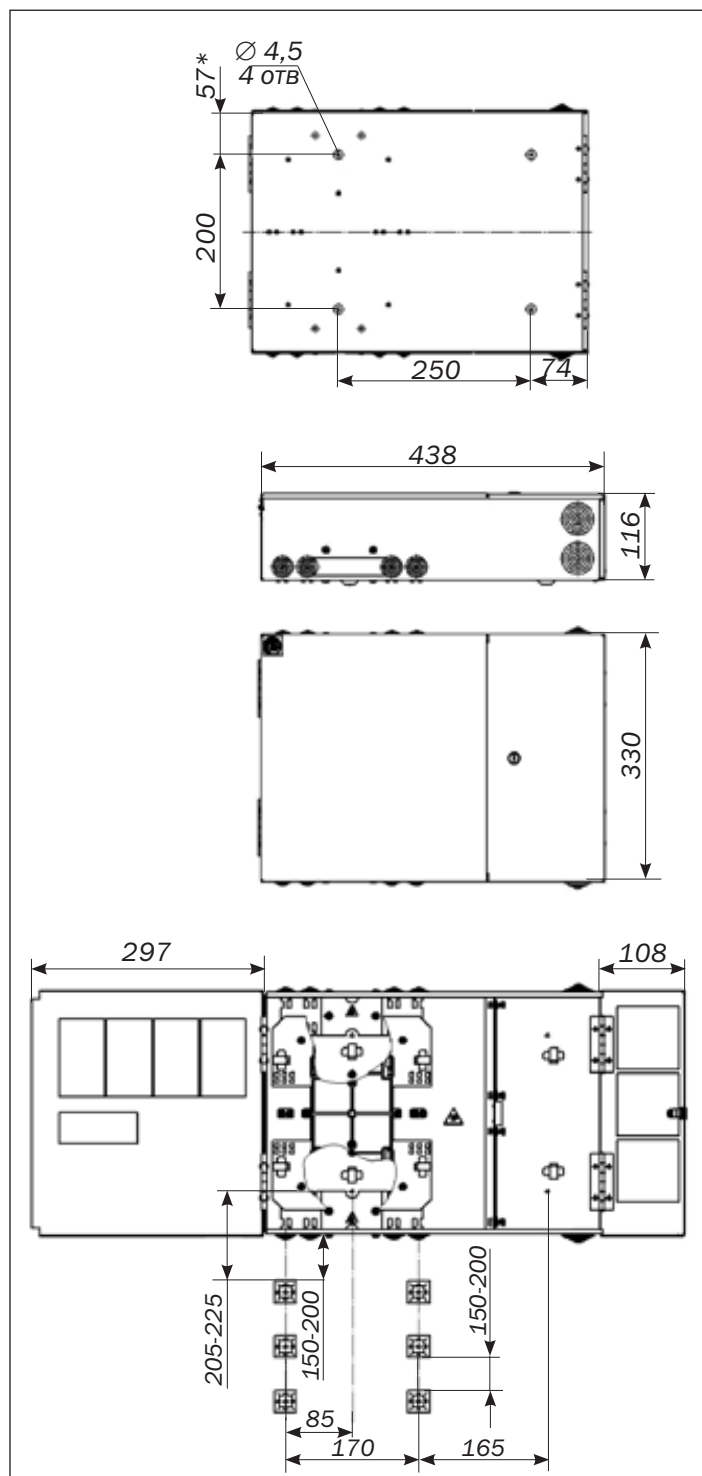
Габаритные и установочные размеры шкафа
